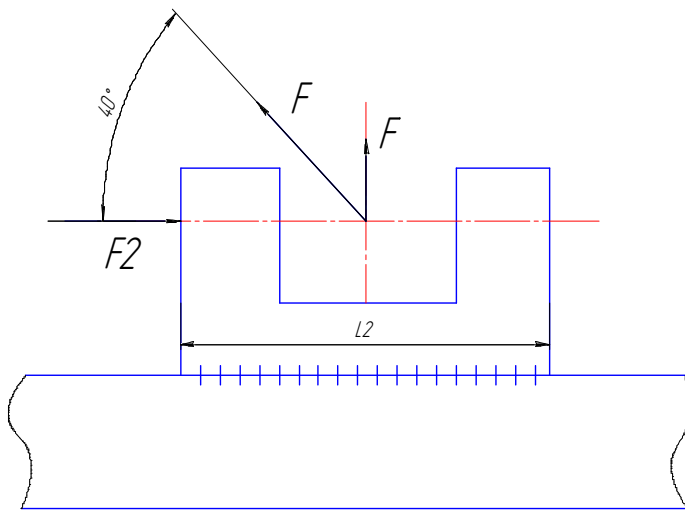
Розрахункова схема зварного шва кронштейна гідроциліндра
